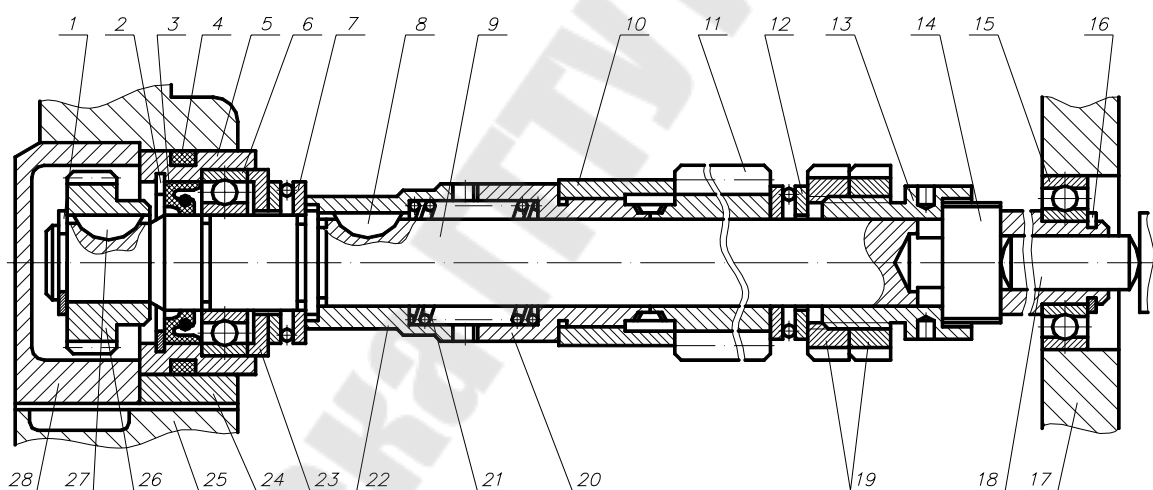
Эскиз сборочной единицы устанавливаемой на шарикоподшипники
